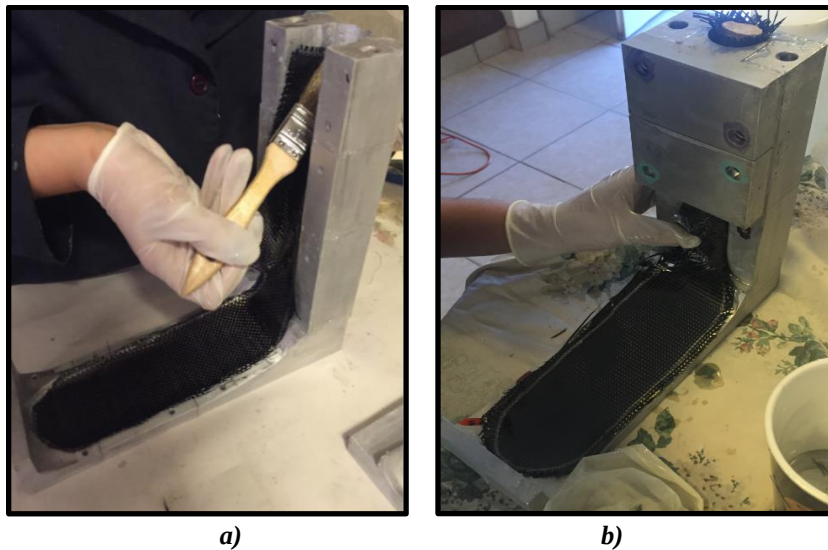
a) Impregnación de resina; b) Sellado de molde.
